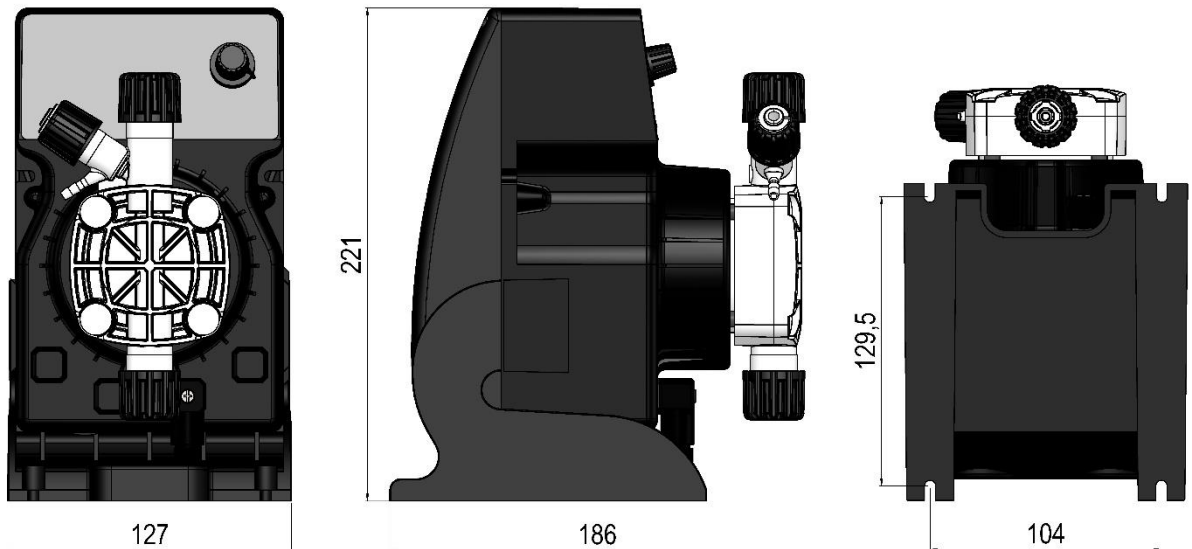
Bomba PBM, con base de soporte (dimensiones indicadas en mm).
